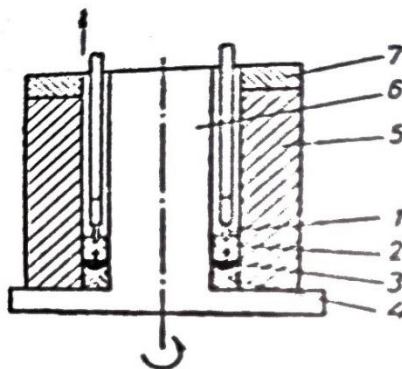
ЕШН внутрішньої циліндричної поверхні: 1 – електрод; 2 – шлакова ванна; 3 – металева ванна; 4 – наплавлений шар; 5 – заготівля; 6 – мідний стрижень, що охолоджується; 7 – втулка вивідна
